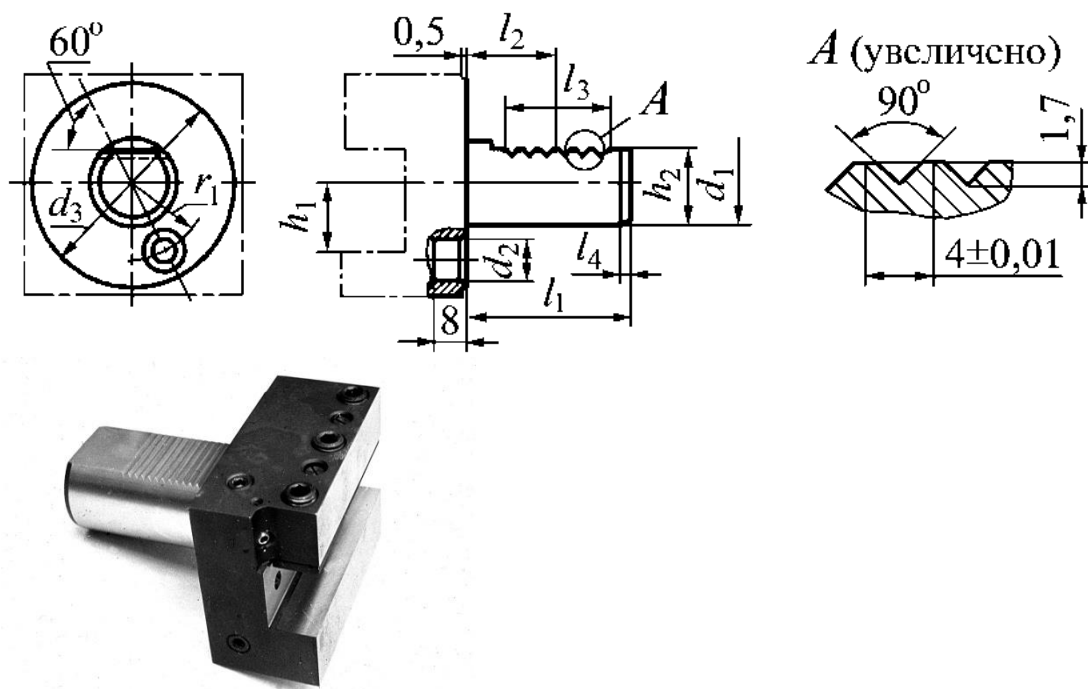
Основные размеры, мм, цилиндрических хвостовиков по ГОСТ 24900-81 и стандарту DIN 69880 для станков токарной группы
